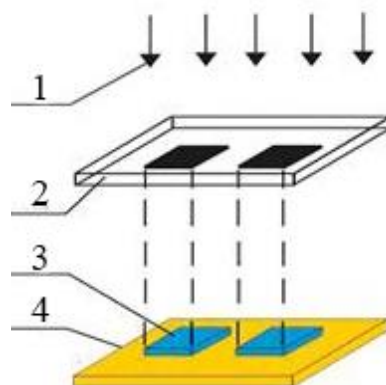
Негативний фоторезист [7]: 1 – випромінювання; 2 – фотошаблон; 3 – фоторезист; 4 – підкладка
